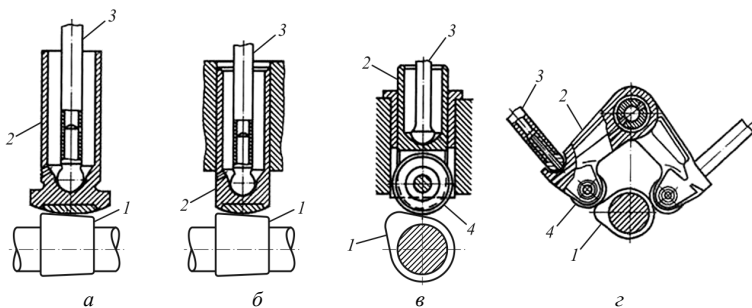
Типы толкателей: *а* – грибовидный; *б* – цилиндрический; *в* – цилиндрический роликовый; *г* – рычажный роликовый; 1 – кулачок распределительного вала; 2 – толкатель; 3 – штанга; 4 – ролик
